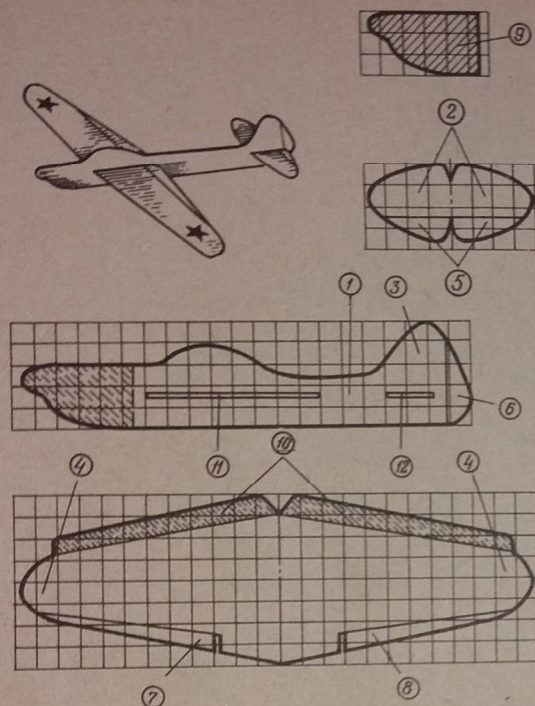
Модель самолета Як-3: 1— фюзеляж; 2— стабилизаторы; 3— киль; 4— крылья; 5— руль высоты; 6— руль поворота; 7— левый элерон; 8— правый элерон; 9— груз из картона; 10— клапаны, образующие переднюю кромку крыла (при подклеивании); 11— прорезь для крыльев; 12— прорезь для стабилизатора
